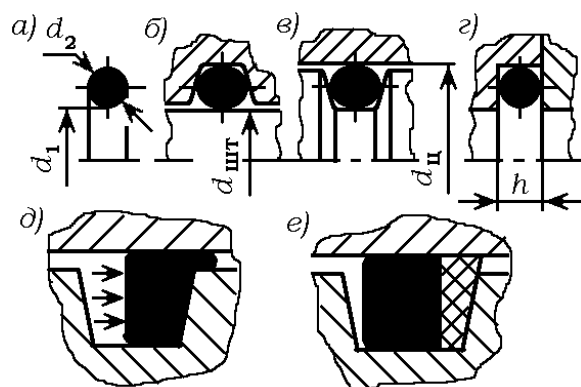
Резиновые кольца круглого сечения по ГОСТ 9833: а) размеры кольца d_1 , d_2 – внутренний и диаметр кольца; б), в), г) варианты установки кольца, $d_{шт}$, $d_{ц}$, h – размеры штока, цилиндра и ширина установочной канавки; д) затягивание резины кольца в зазор под действием давления и подрезание; е) установка защитного фторопластового кольца
